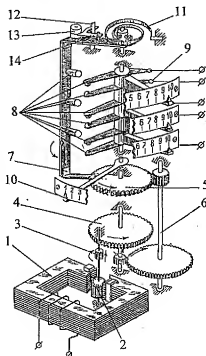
Конструкция реле времени типа RBM-12 с синхронным мотором и втягивающимся (как соленоид) ротором: 1 — статор двигателя; 2 — ротор; 3, 4, 5 — зубчатые колеса; 6 — редуктор; 7 — поворотная рамка с контактами; 8 — контакты; 9 — поводок уставки положения неподвижных контактов (выдержки времени); 10 — буксирная стрелка; 11 — возвратная пружина; 12 — упор; 13 — замок; 14 — пружина
